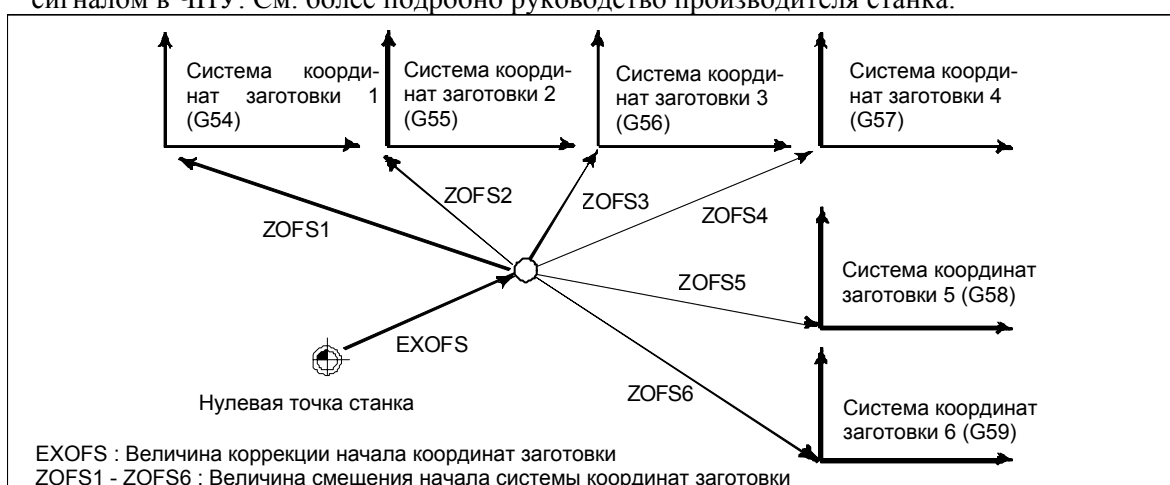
(а) Изменение значения внешней коррекции начала координат заготовки или значения коррекции начала координат заготовки
